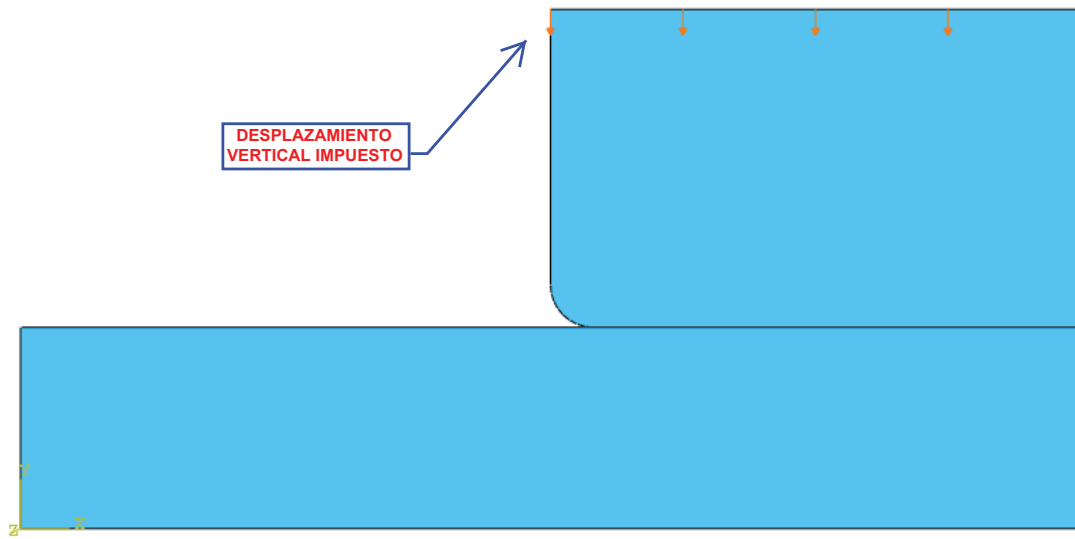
Disposición de la carga de ensamblaje en el modelo.
